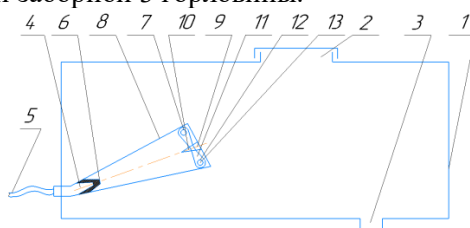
Схема установки мешалки в резервуаре опрыскивателя: 1 – резервуар опрыскивателя; 2 – заливная горловина; 3 – заборная горловина; 4 – гидравлический жиклер; 5 – рукав; 6 – выходное сопло жиклера; 7 – лопастная крыльчатка; 8 – прутковый каркас; 9 – обойма с осью
